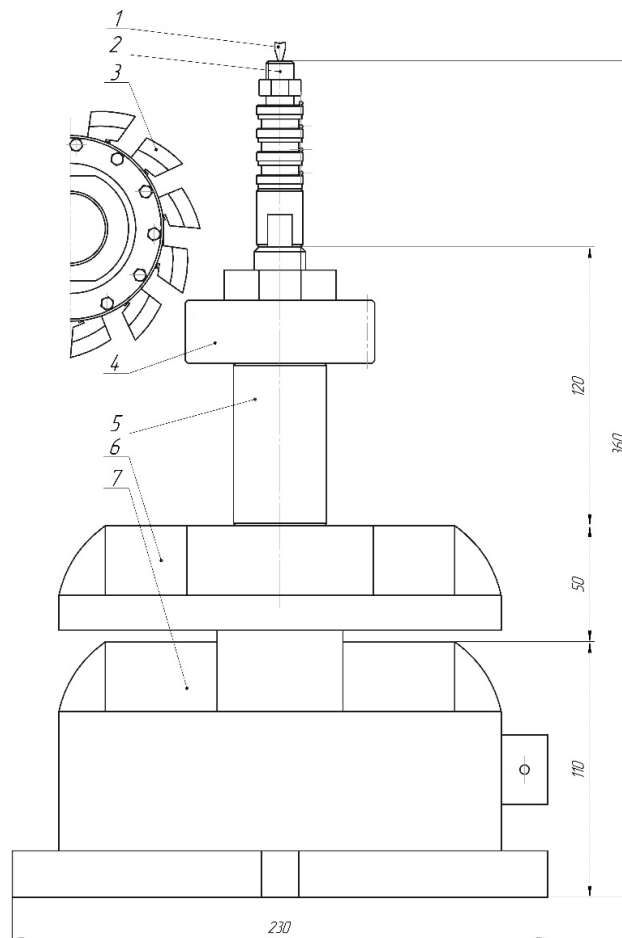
Эскиз приспособления для закрепления образцов, имитирующих целое зубчатое колесо
